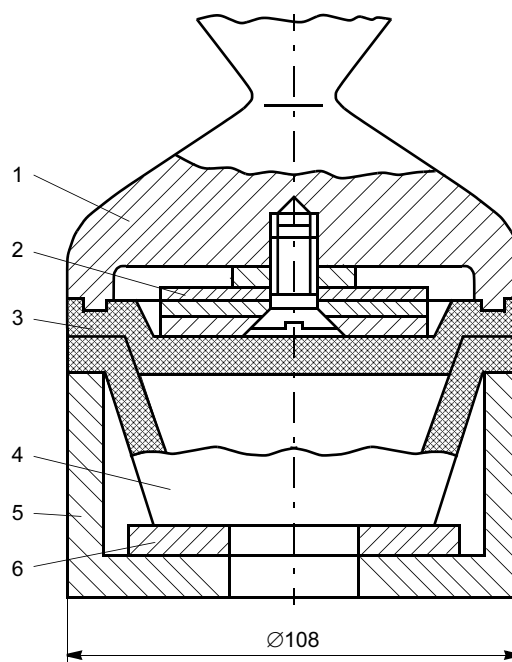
Схема сварки цилиндрического изделия контурным волноводом с акустическим экраном
